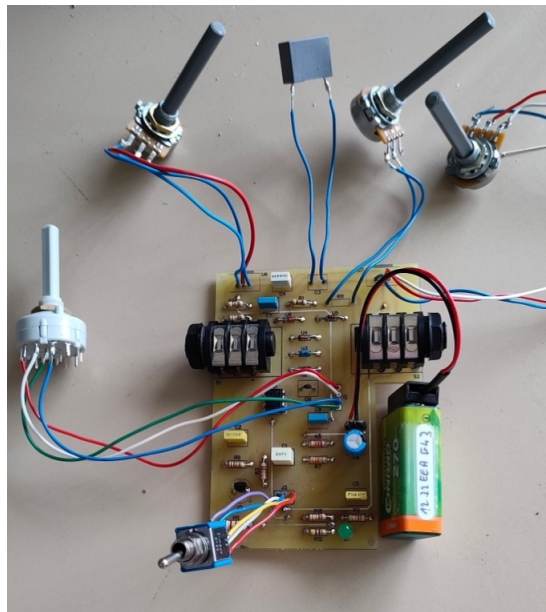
Prototype final de la carte électronique de la pédale Ibanez Tubescreamer
